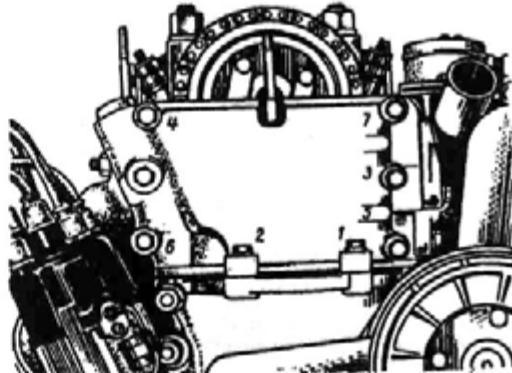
Последовательность затяжки болтов крепления верхней крышки звездочек
